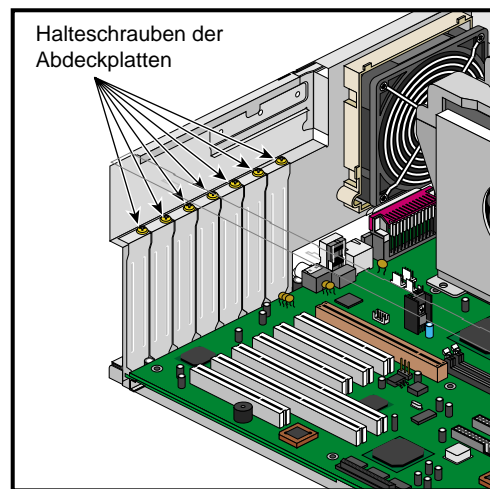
Lage der Halteschraube für die Erweiterungssteckplatz-Abdeckplatte
